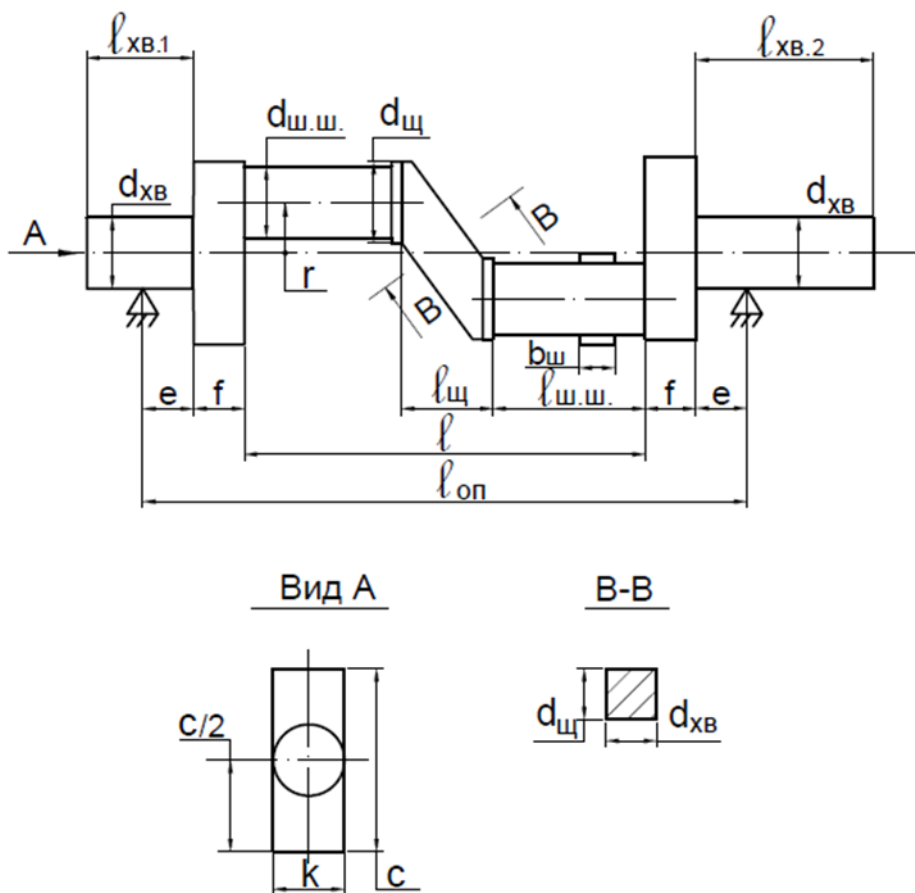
Эскиз коленчатого вала поршневого компрессора:
